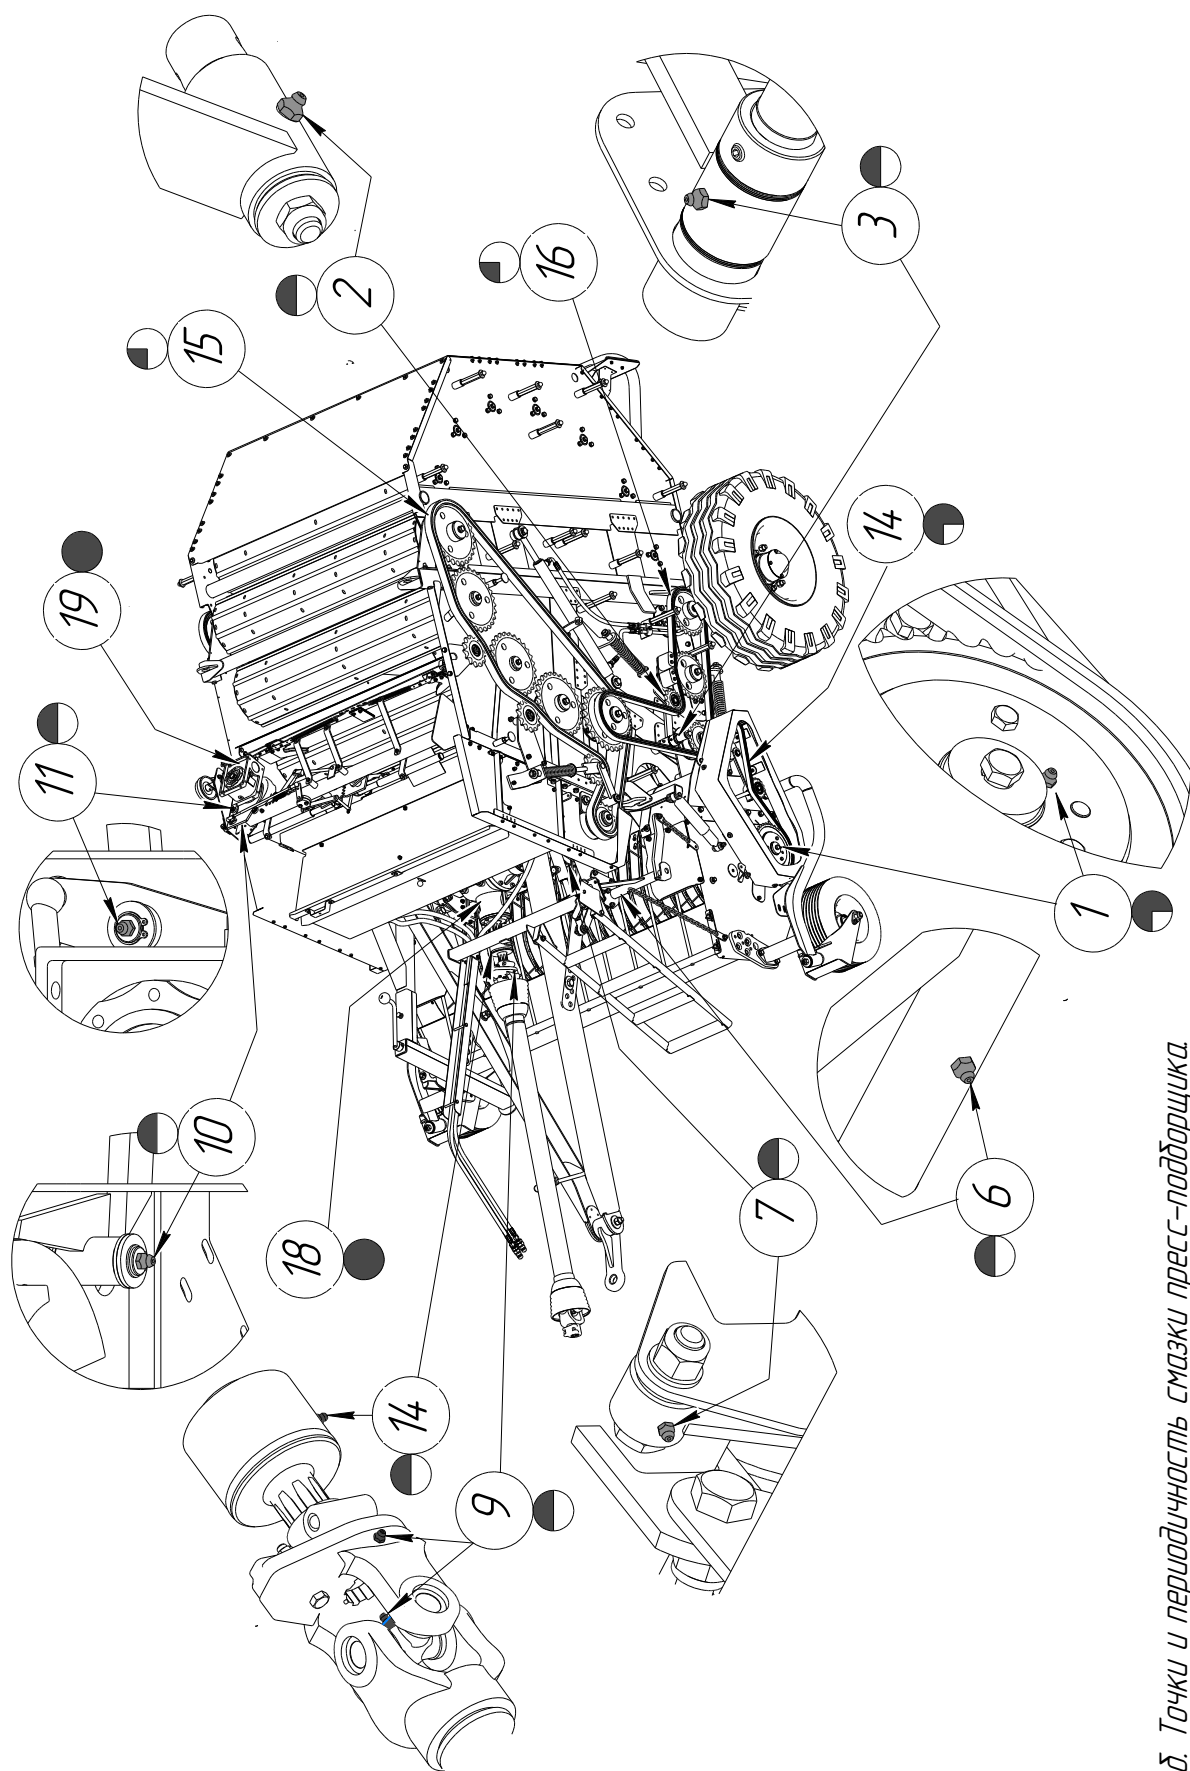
д. Точки и периодичность смазки пресс-подборщика
